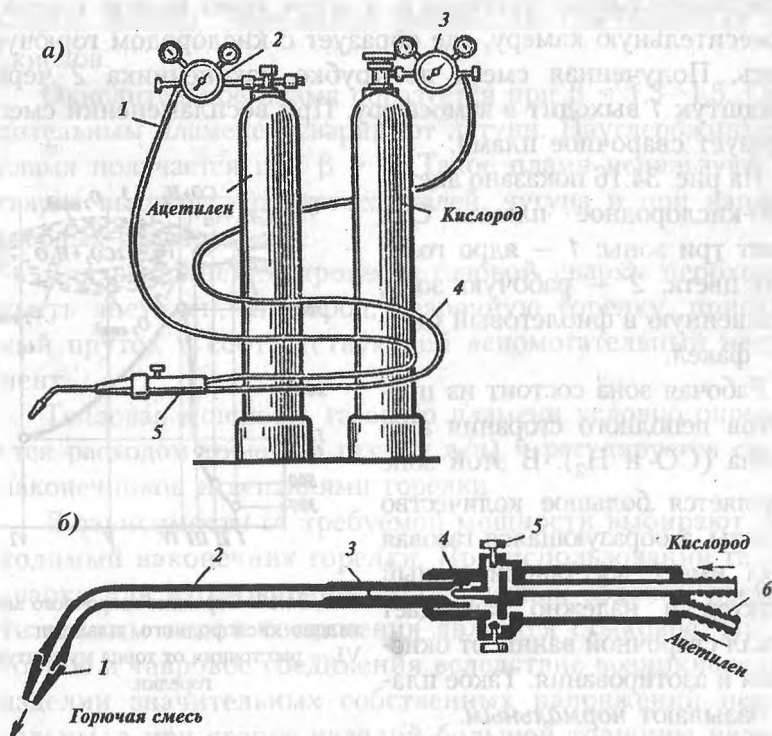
Оборудование газосварочного поста: а — схема газосварочного поста с питанием от баллонов: 1 — шланг подачи ацетилена; 2 — редуктор ацетиленовый; 3 — редуктор кислородный; 4 — шланг подачи кислорода; 5 — сварочная горелка; б — схема инжекторной горелки
